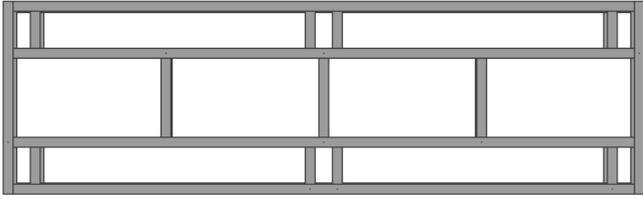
Estructura viga laminada soldada. Vista superior. Modelo de elaboración propia.
